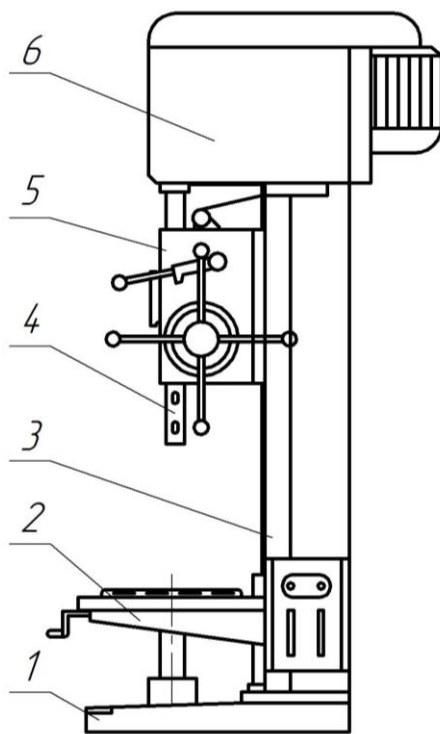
Загальний вигляд вертикально-свердлильного верстата
